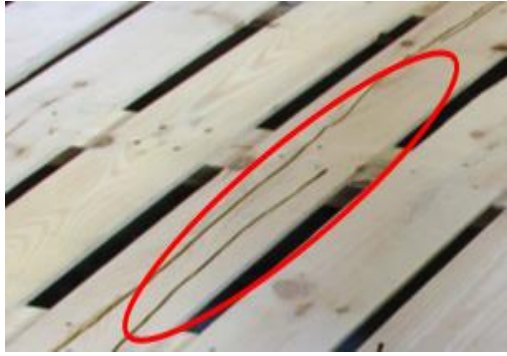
Ejemplo Grietas delgadas siempre y cuando el elemento se encuentre fijo
